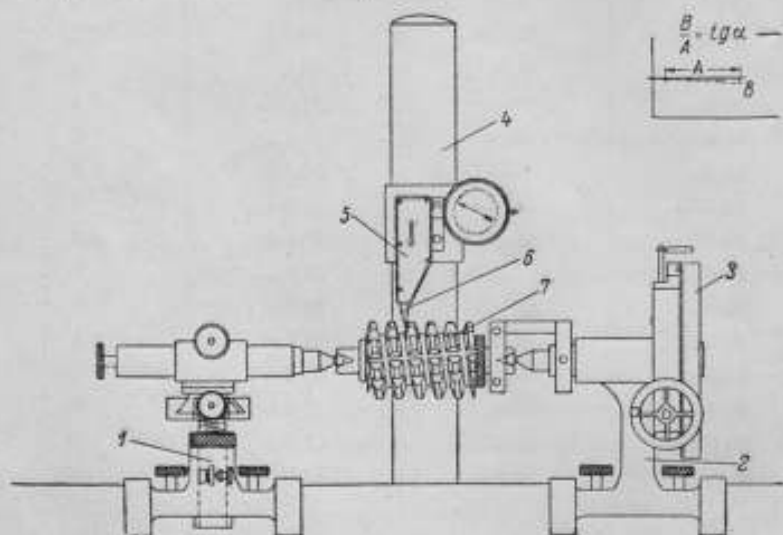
Контактное приспособление и стол с поворотным и подвижным центрами для измерения червячных фрез.
